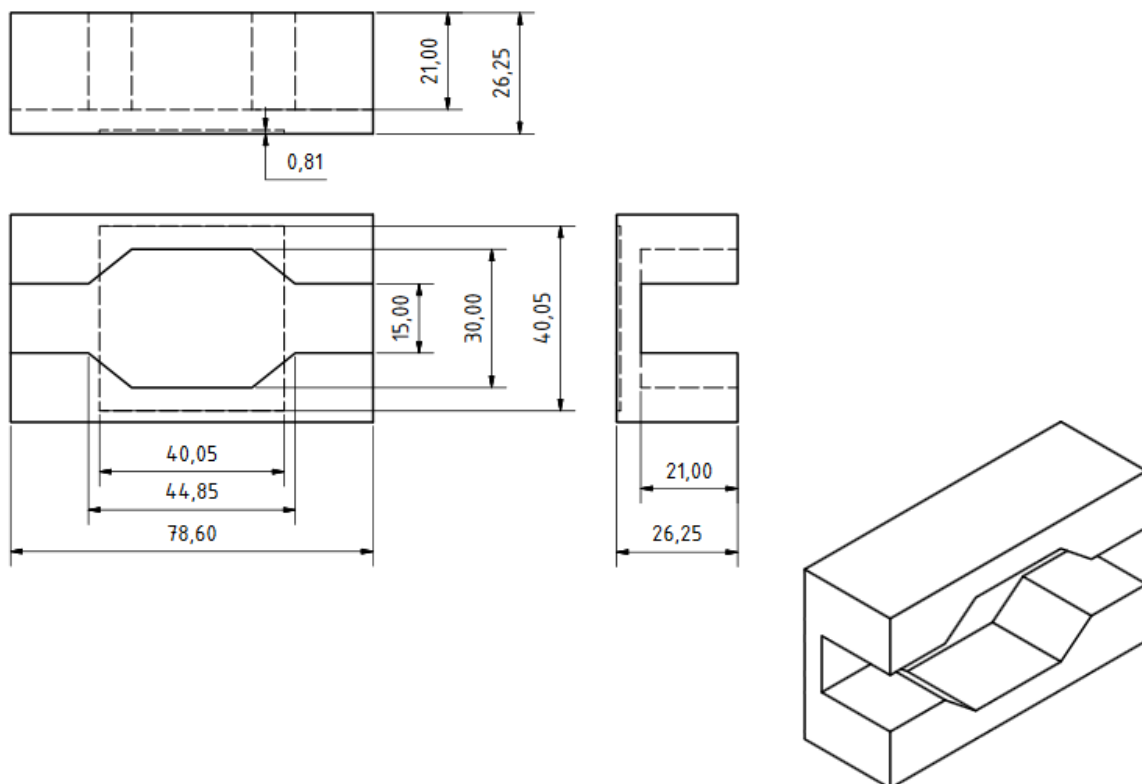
technische Zeichnung des Aluminiumkühlmantels, welcher das Enzymtransformationsmodul umschließt mit sowie skizzierter 3D-Ansicht. Abgeschlossen wird der Aluminiummantel durch einen in dieser Abbildung nicht gezeigten passenden Aluminiumdeckel.
